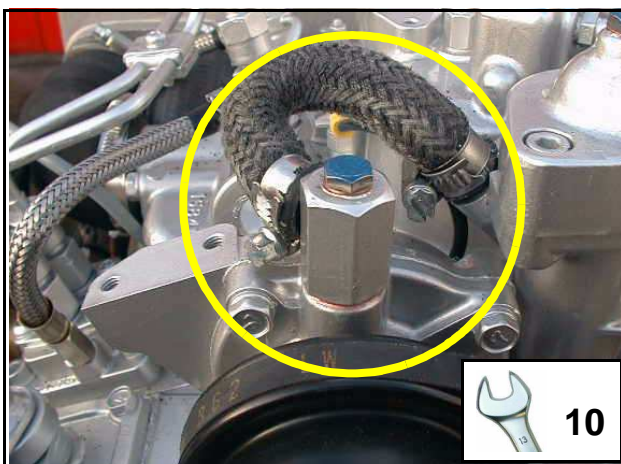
Entlüftungsschraube am Rohrstutzen
